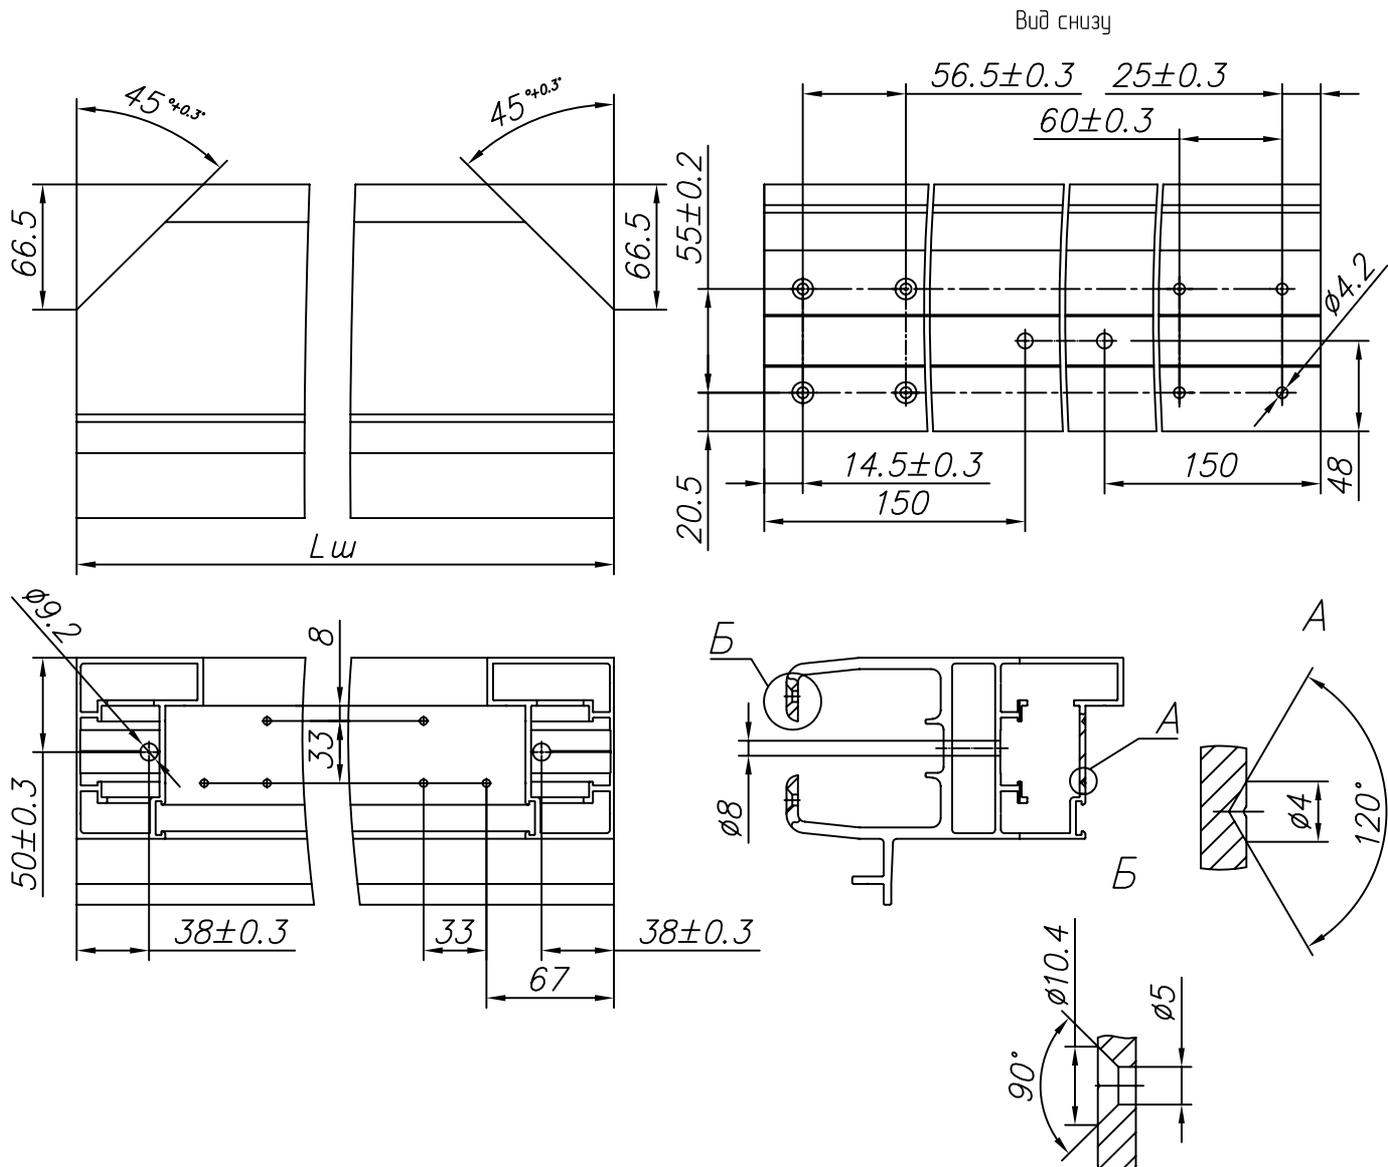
Изготовление шины для пассивной(опорной) створки (открытие влево)
